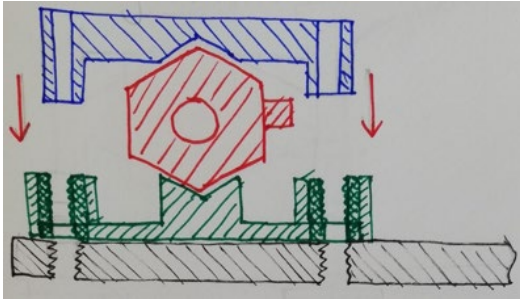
Skizze des Befestigungsmechanismus für das Kugelventil
